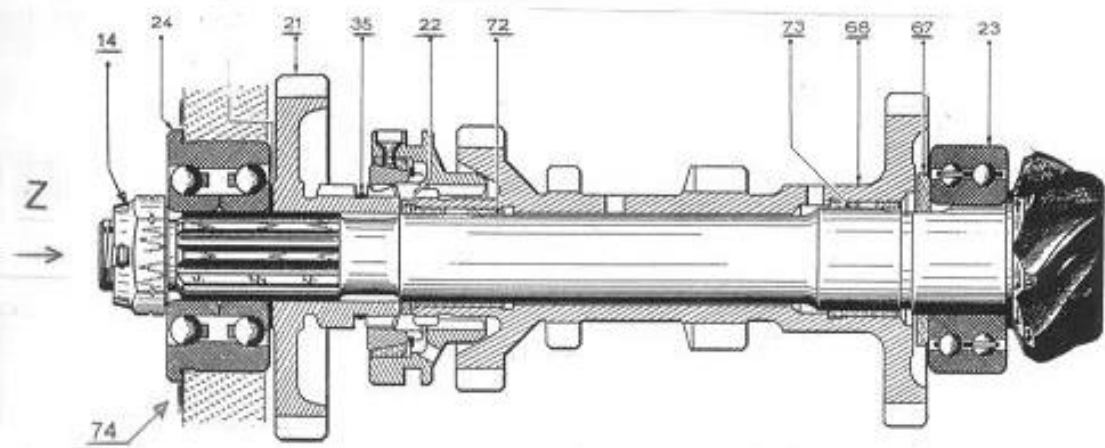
Ensemble de l'arbre du pignon d'attaque
